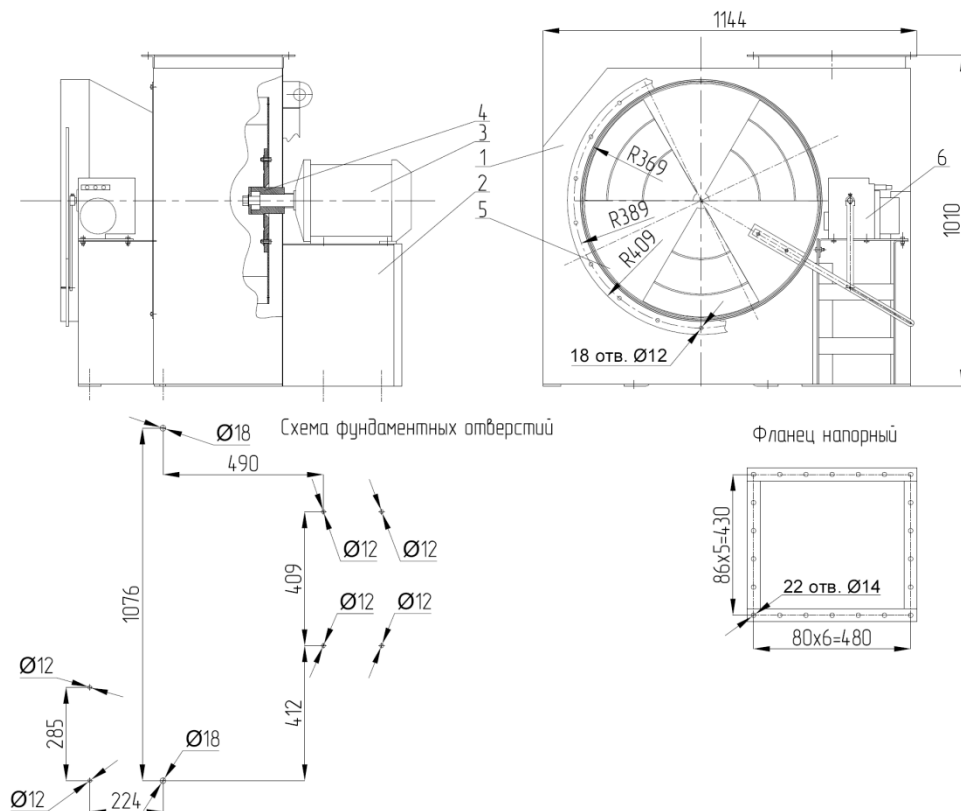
Дымосос ДН-6,3 (1-корпус, 2-рама, 3-электродвигатель, 4-рабочее колесо, 5-аппарат шиберный, 6- привод шибера.
